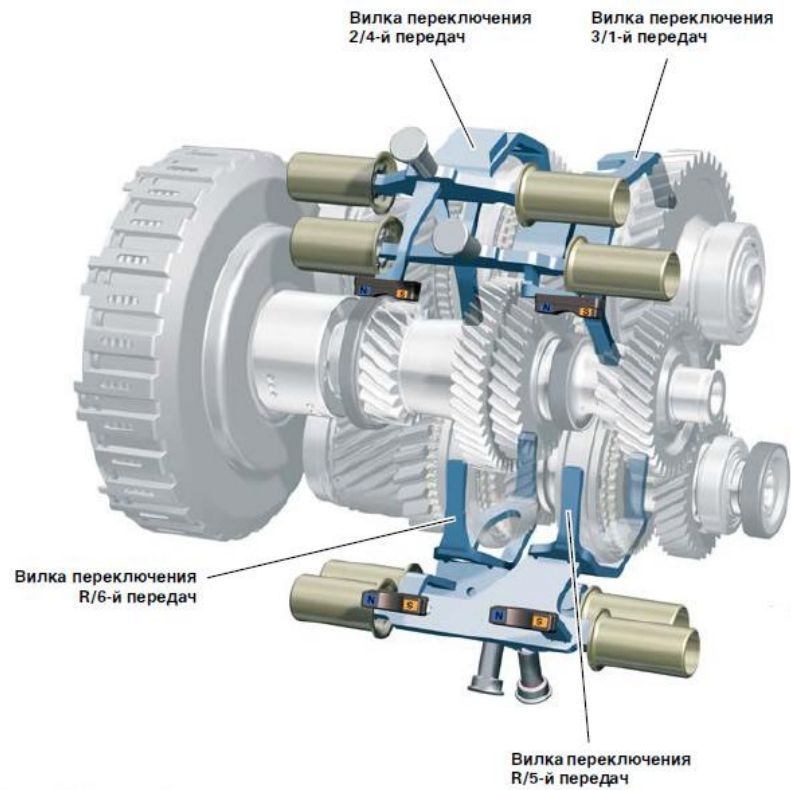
Переключение блоков зубчатых колес с помощью вилок и гидроцилиндра
